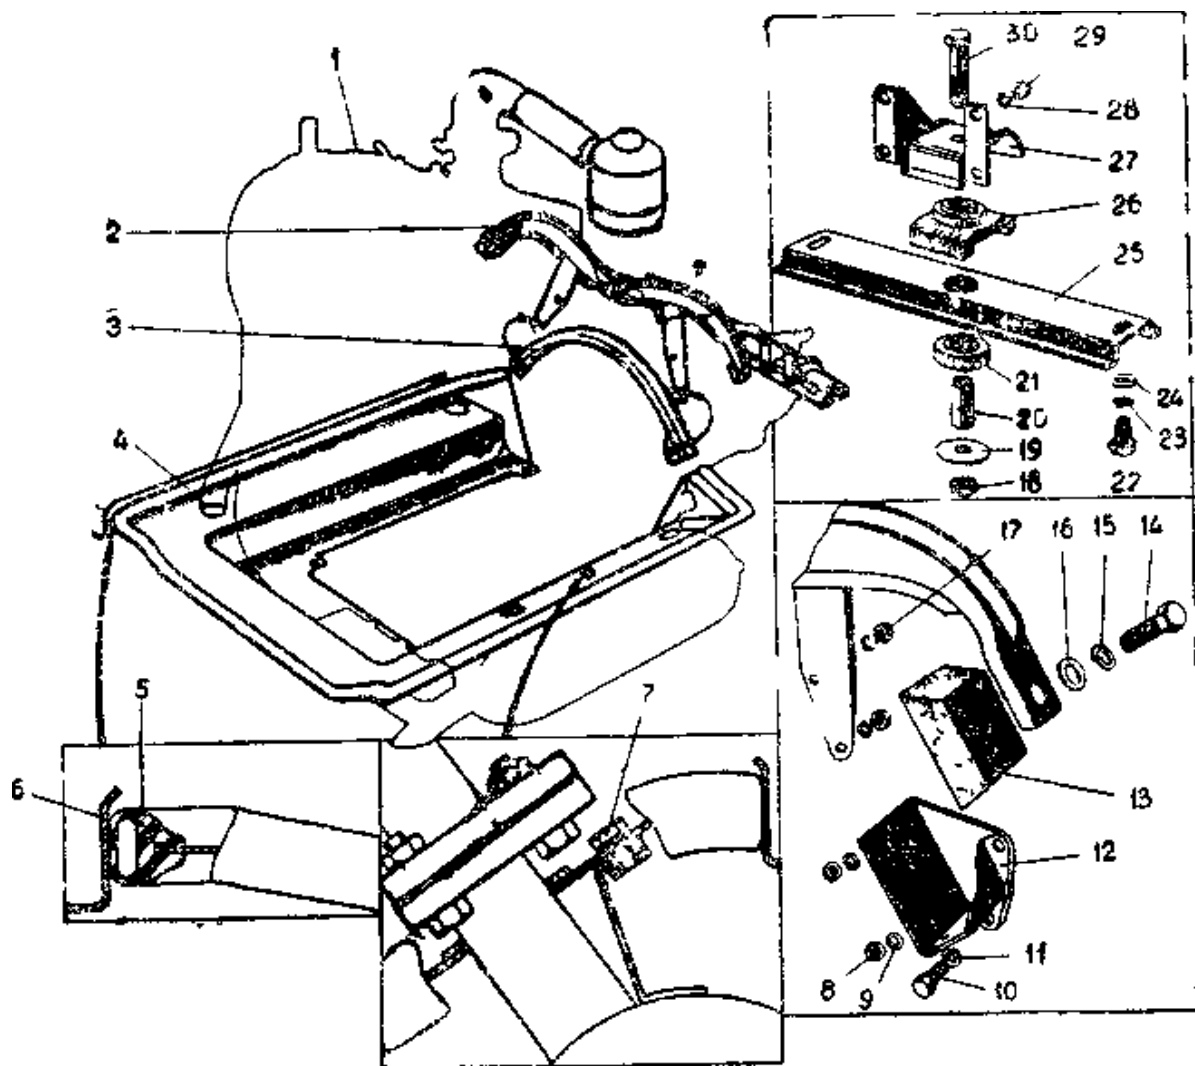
Подвеска силового агрегата и брызговик двигателя:
